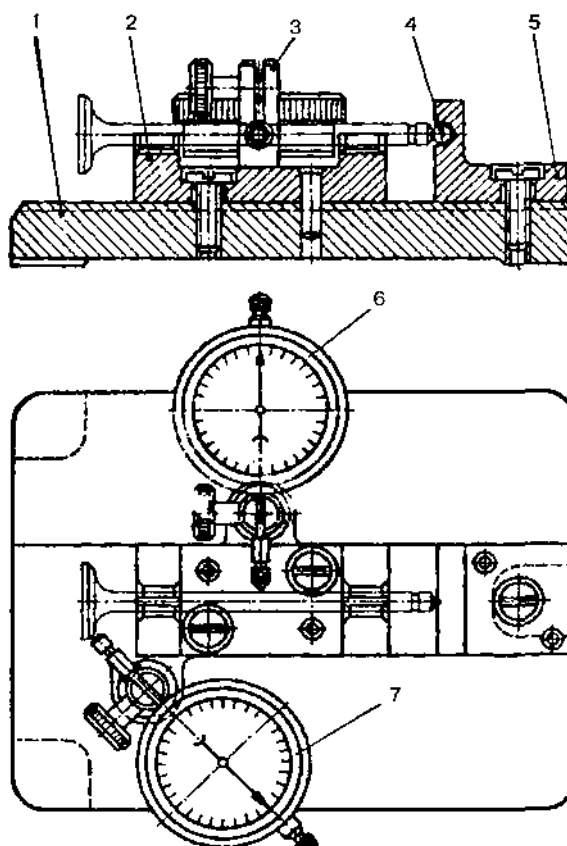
Проверка клапана на concentricity рабочей фаски головки и стержня:
